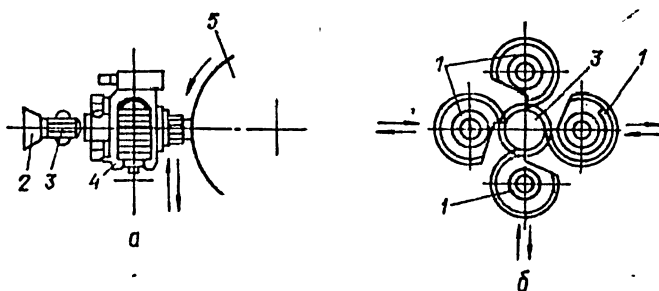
Схема установки и работы резьбопарезной самооткрывающейся головки с круглыми гребенками.
